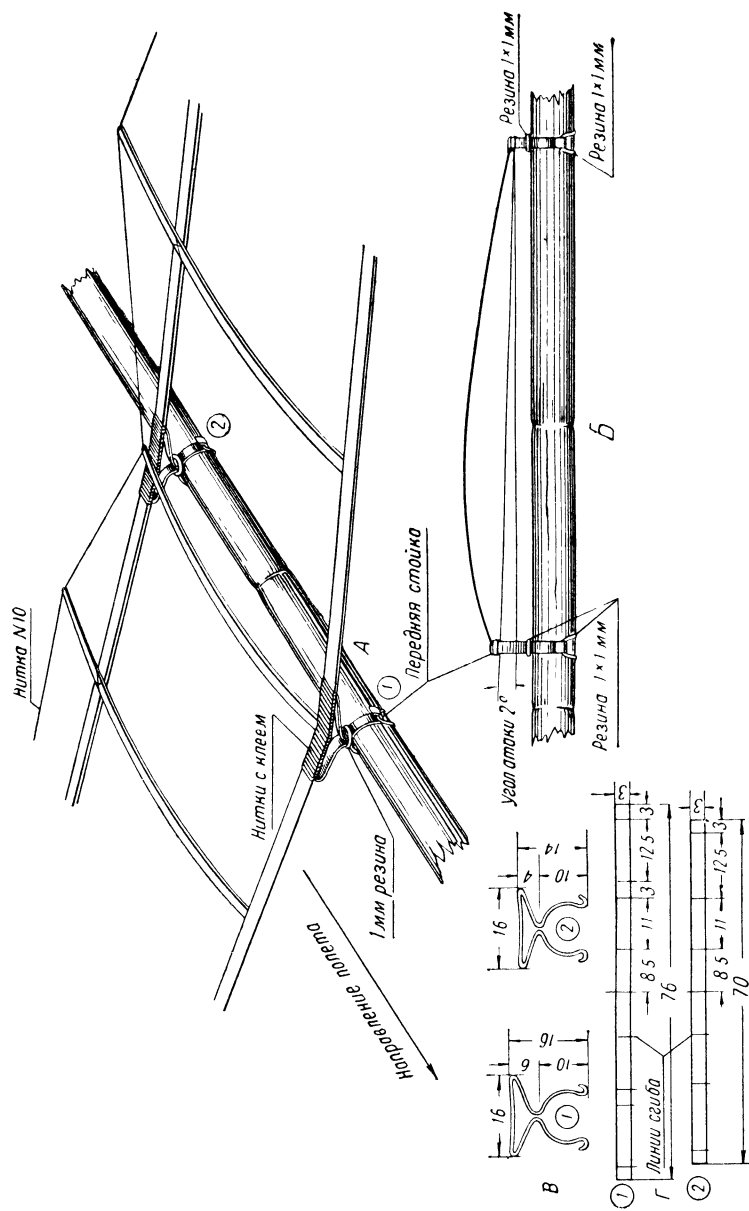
Крепление крыла: А — общий вид; Б — вид крепления сбоку; В — передняя и задняя стойки крепления крыла; Г — развертки подкосов
